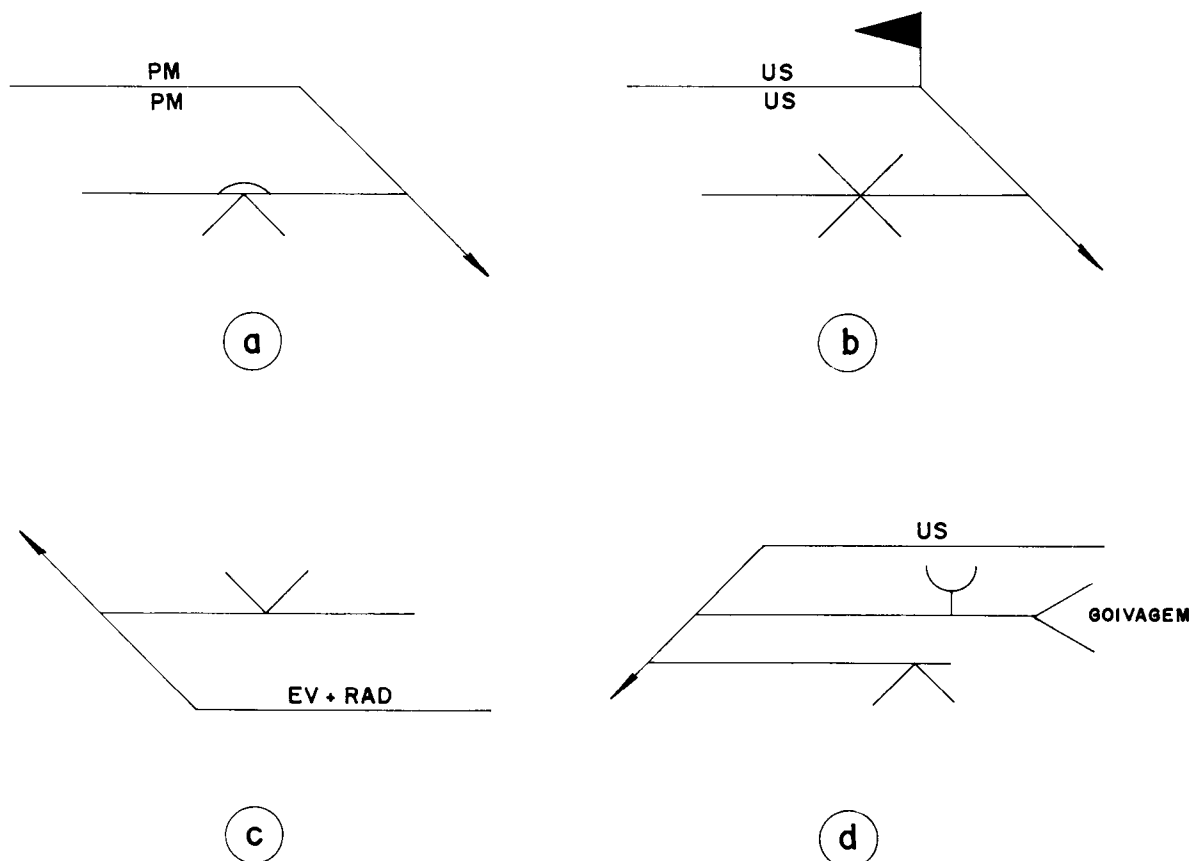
Exemplos de combinação de símbolos de exame não-destrutivo com símbolos de soldagem, significando:
